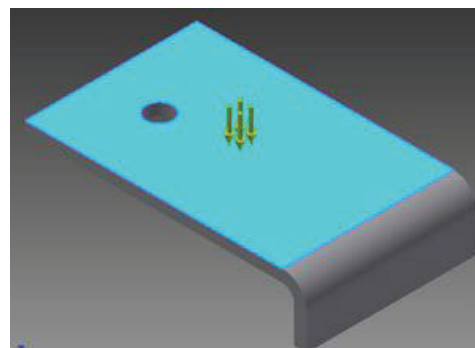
78 Restricciones y Cargas Aplicadas en el Soporte
